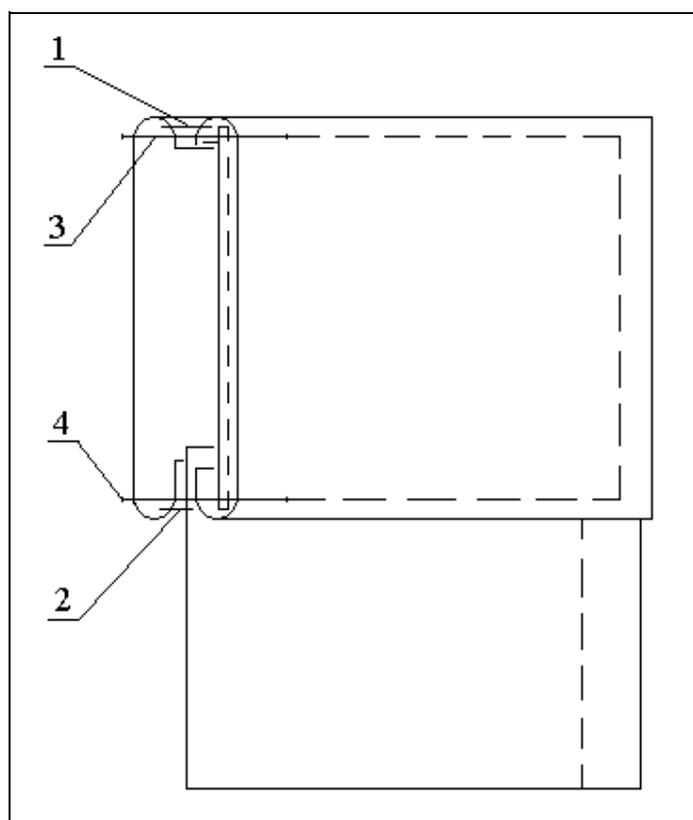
Сборочная схема обработки и соединения воротника-стойки с горловиной изделия (первый способ)
